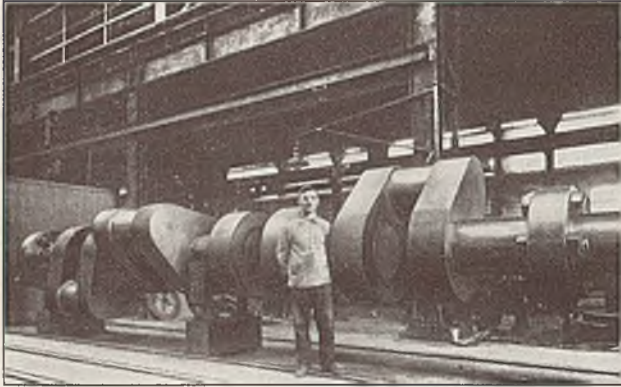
Eine 8fach gekröpft Kurbelwelle mit Kompressorwelle für und fertig bearbeitet, Gewicht ca. 47000 kg, Länge 14200 mm, κ -Rad. 650 mm, geliefert für Deutsche Werke Kiel
